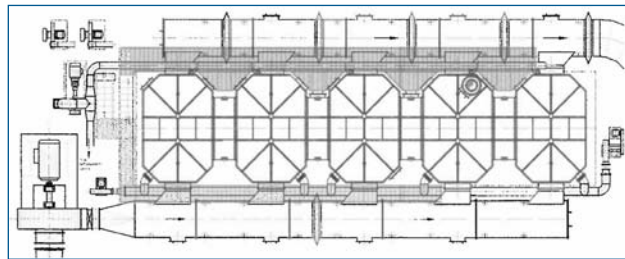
Disegno tecnico del combustore termico-rigenerativo.
